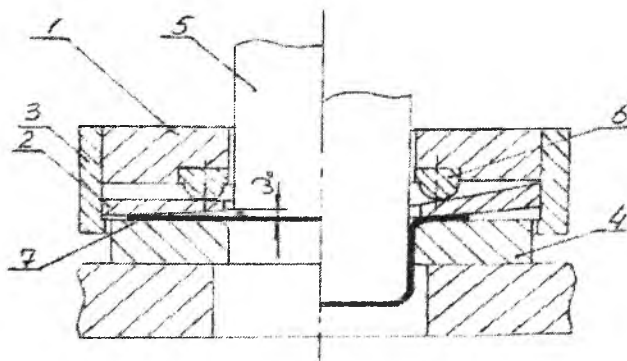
Конструкция штампа для вытяжки тонколистового материала с использованием упруго прижима. 1-кольцо опорное; 2-прижим упругий; 3-обойма; 4-матрица; 5-пуансон; 6-выступ кольцевой; 7-заготовка.
